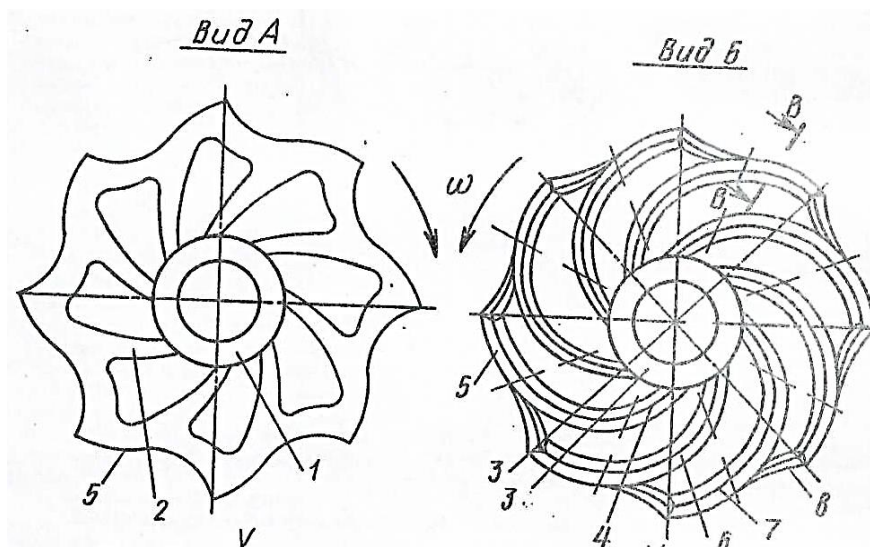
Вид А і вид Б на рис 2.5
